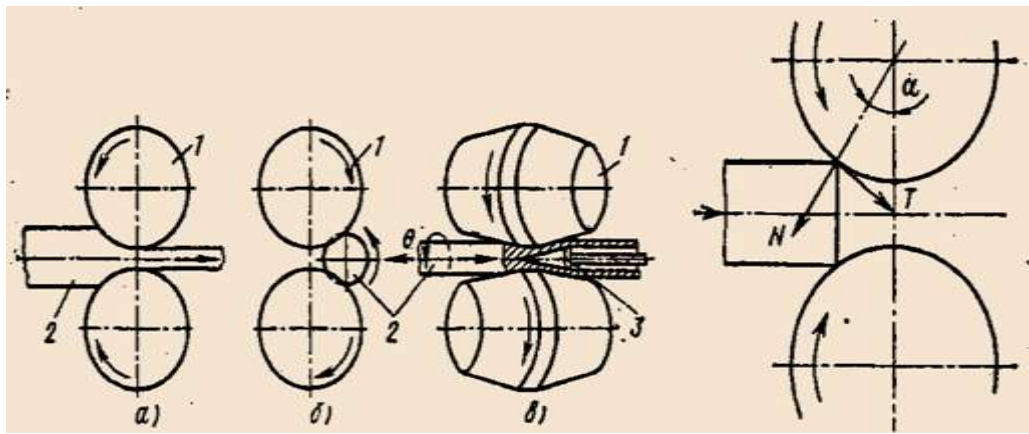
Основные виды прокатки и схема действия сил в момент захвата металла валками: а – продольная; б – поперечная; в – поперечно-винтовая; 1 – валки; 2 – заготовка; 3 – оправка; N – нормальная сила; T – сила трения.
